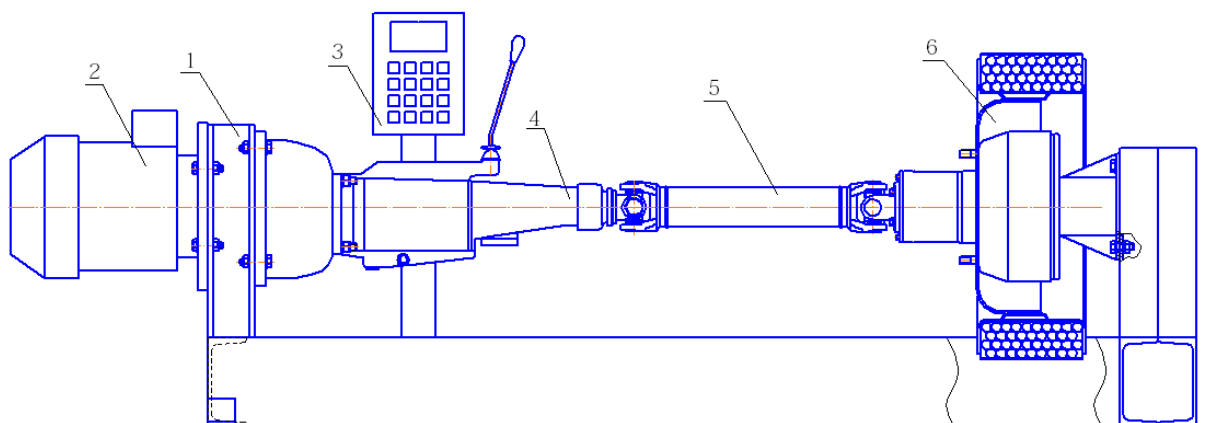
Схема стенда испытания и обкатки КП
